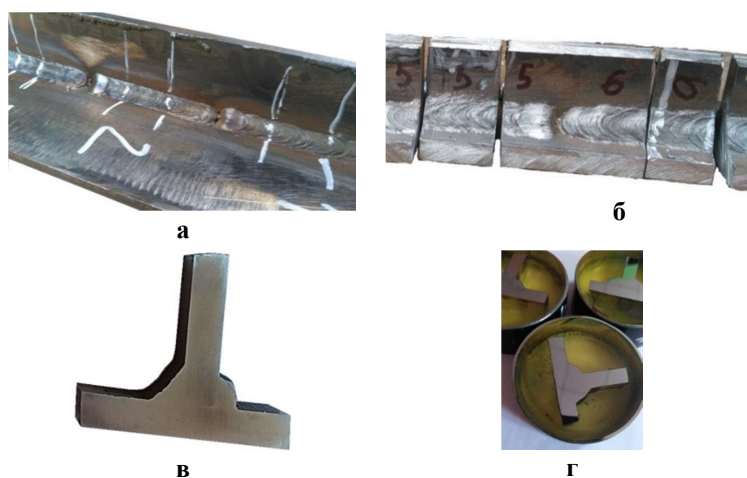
сварные швы таврового соединения (а), вырезанный образец (б), образец для заливки (в), залитые образцы (г)
